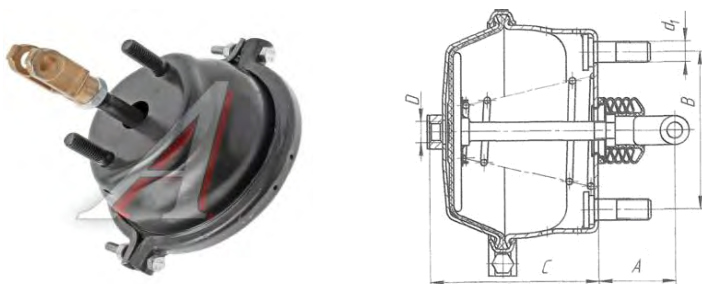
Общий вид и устройство пневмокамеры 25.3519101
